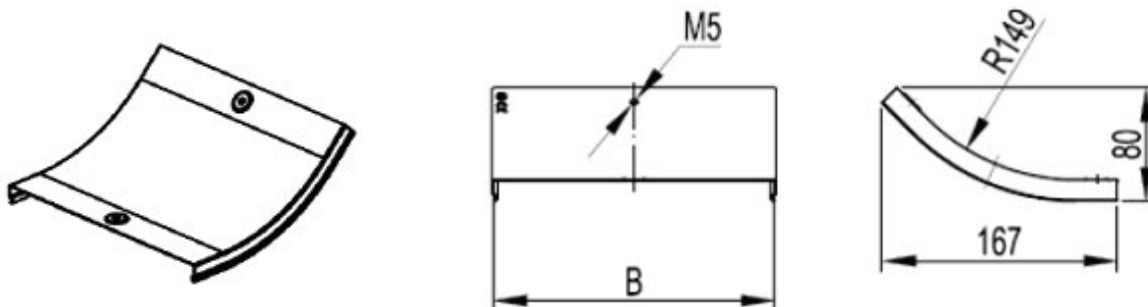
Крышка CS 45 на угол вертикальный внутренний 45°
